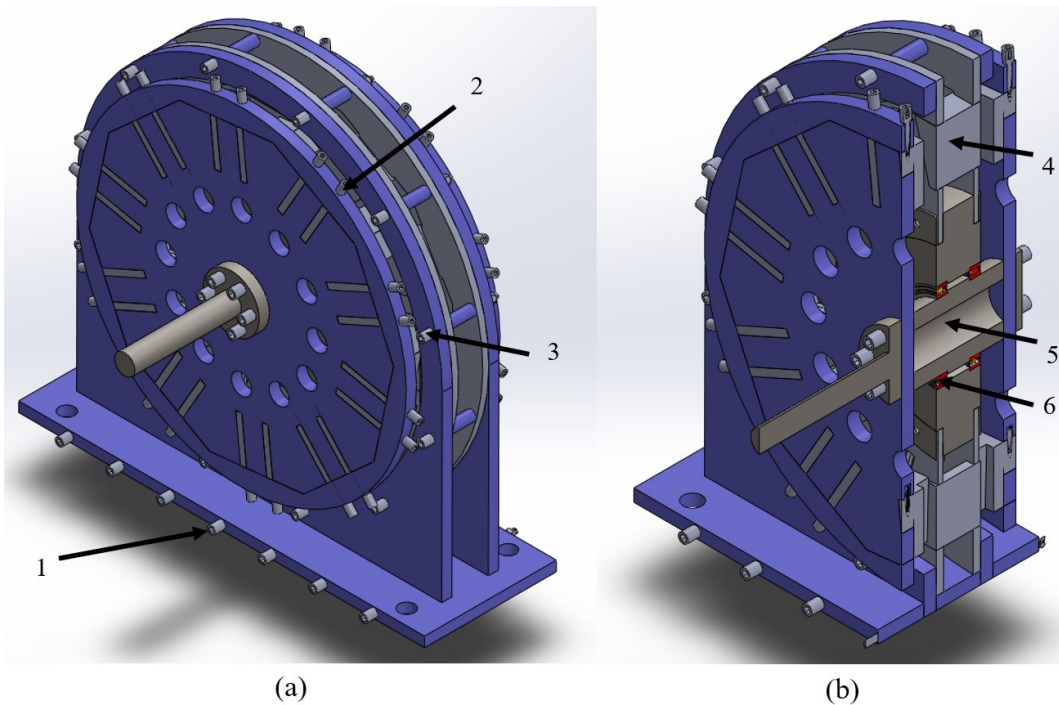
Montagem da MRSFV proposta com todas as peças: 1 – Eixo da máquina; 2 – anel de fixação dos módulos no rotor; 3 – polo do rotor; 4 – polo do estator; 5 – Enrolamentos de campo e de armadura; 6 – Suporte da máquina; 7 - base da máquina para prender na bancada.
